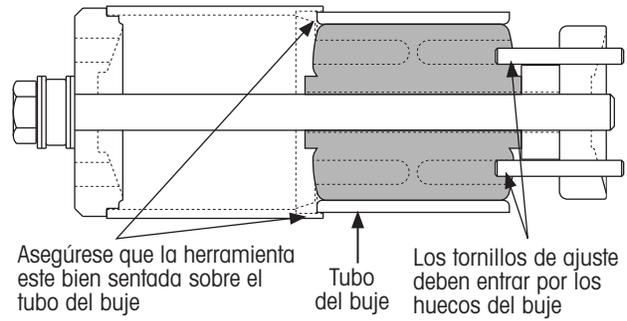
Asegúrese de que la herramienta esté perpendicular al tubo de buje
